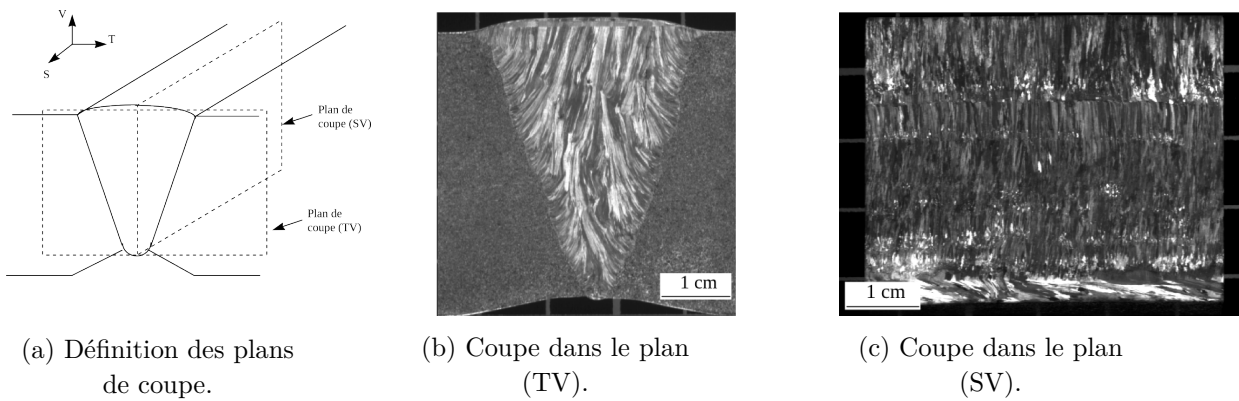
Macrographie d’une soudure industrielle en acier austénitique ([Chassignole, 1999](#)).
